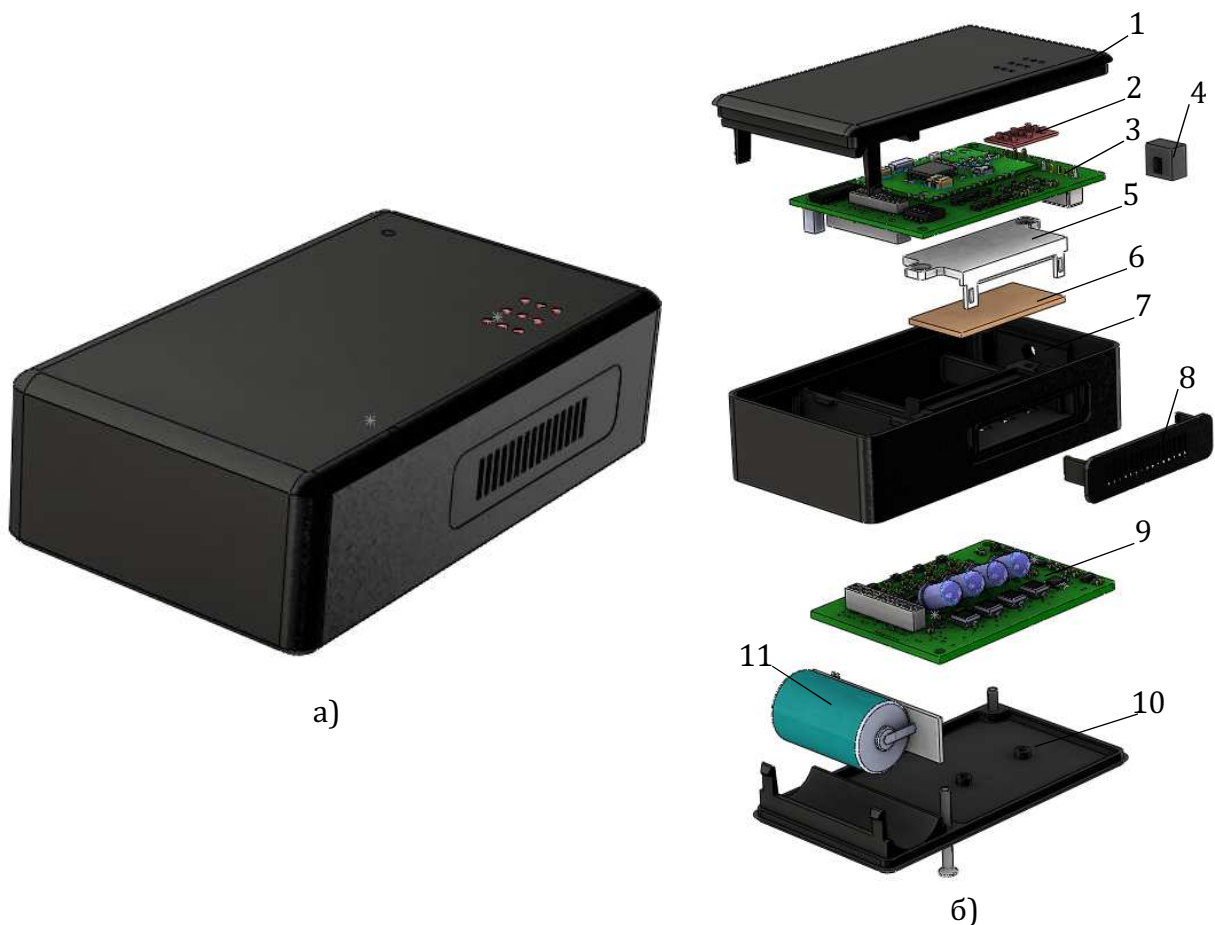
Внешний вид и конструкция датчика БТК. а) – внешний вид датчика; б) – конструкция датчика БТК: 1 – верхняя крышка; 2 – индикаторное окно; 3- плата расширения; 4 – рычажок питания; 5 – крышка измерительного отсека; 6 - хемочип; 7 – корпус; 8 – решетка; 9 – плата датчика; 10 – нижняя крышка; 11 – плата питания.
